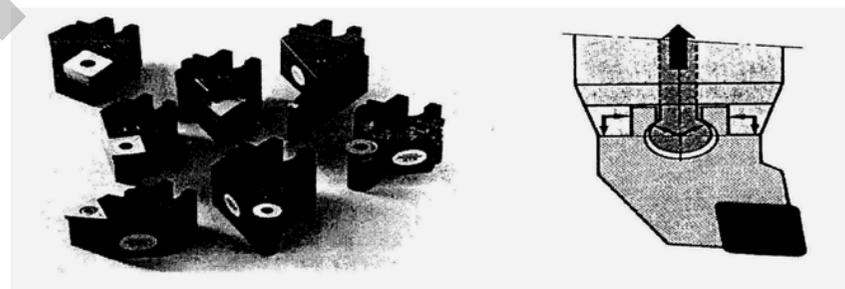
Фотография резцовых блоков и схема их закрепления в устройствах для автоматической смены инструмента
